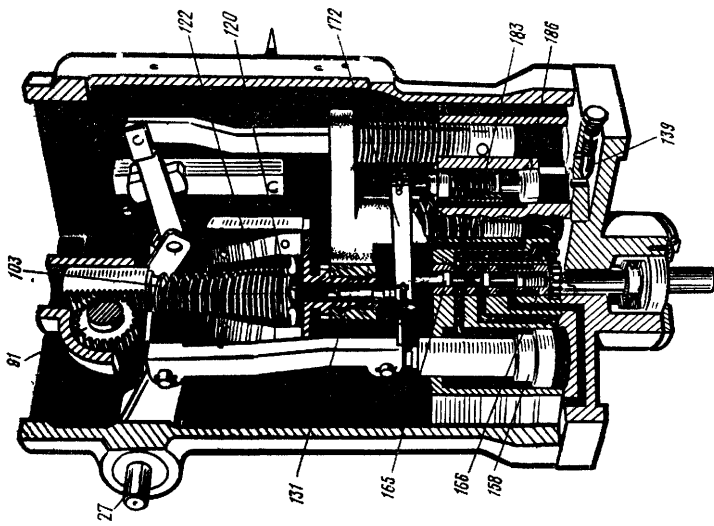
27 — выходной вал; 91 — вал-шестерня установки частоты вращения; 103 — задающая пружина; 120 — муфта с подшипником; 122 — грузы регулятора; 131 — шток; 139 — игла изодрома; 158 — поршень сервомотора; 165 — распределительный золотник; 166 — втулка распределительного золотника; 172 — плавающий рычаг; 183 — пружина изодрома; 186 — принимающий поршень изодрома
